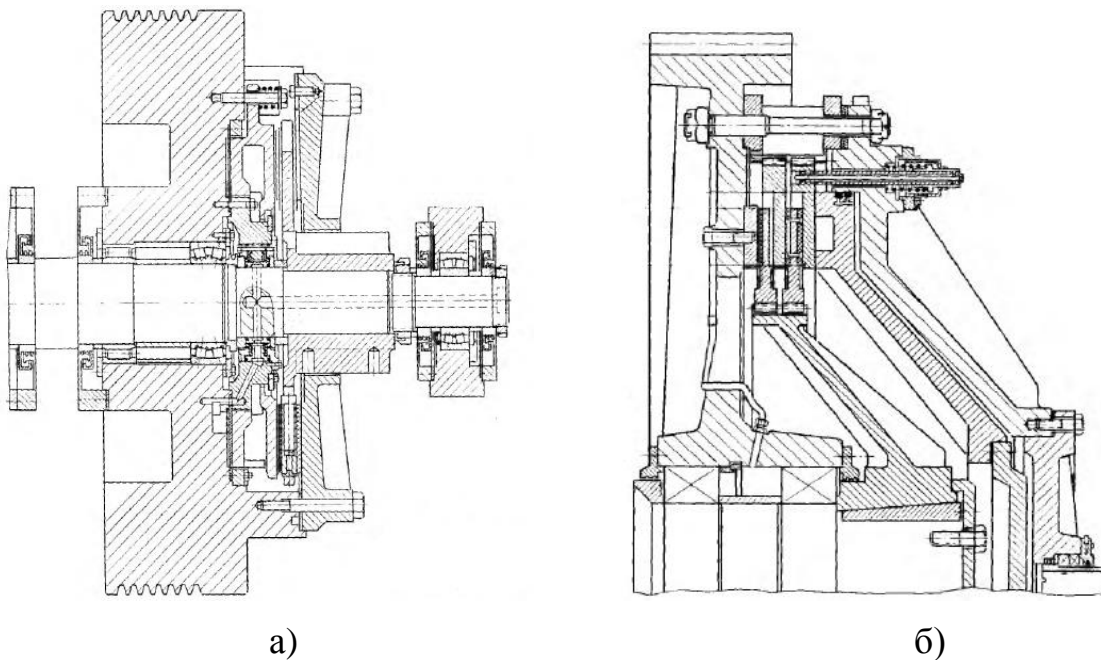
Конструкции муфт: а) межопорная муфта; б) двухдисковая муфта горячештамповочного пресса
